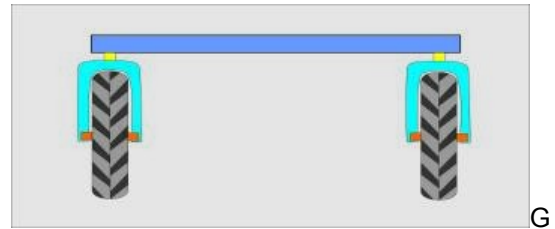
Konstruksi Alat Penabur Benih (tampak samping)
